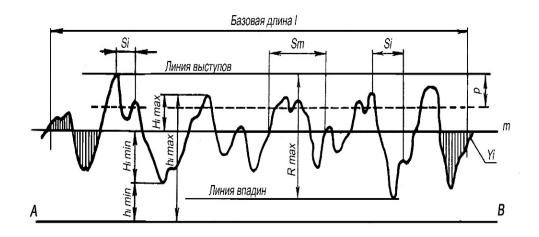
Обобщенный микрорельеф обработанной поверхности
